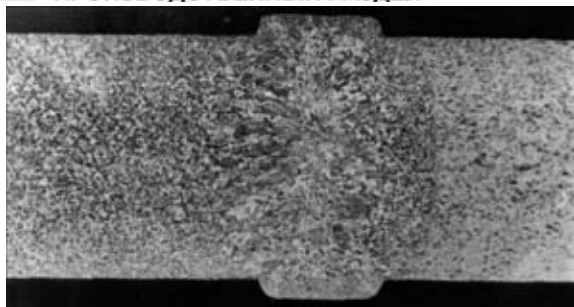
Макрошлиф стыкового сварного соединения сплава ВТ1-0 толщиной 60 мм, выполненного ЭШС пластинчатым электродом
